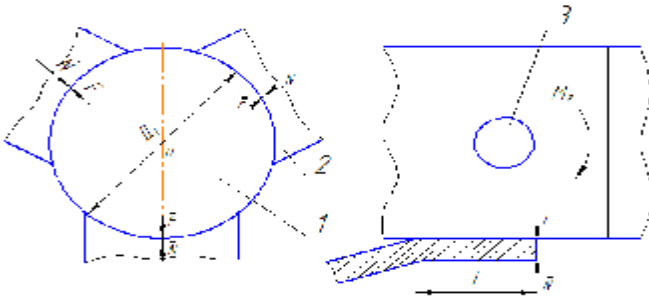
Расчетная схема: 1 – заготовка; 2 – кулачки патрона; 3 – торцевая или концевая фрезы или сверло
